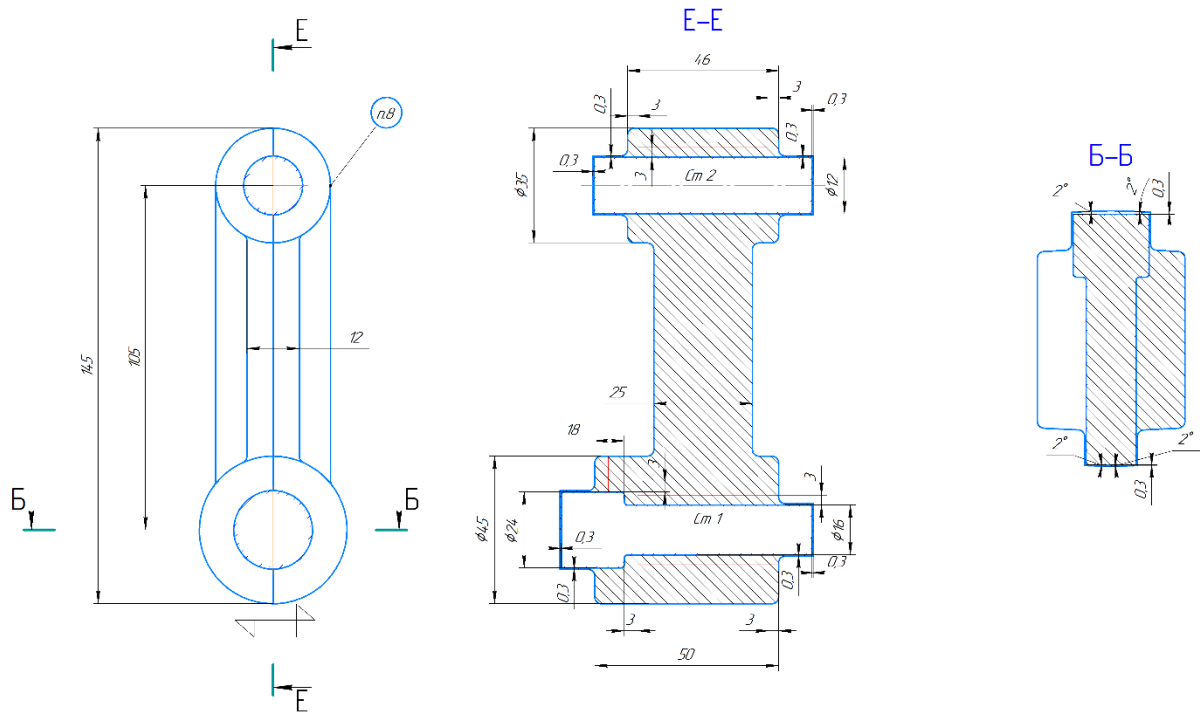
Робоче креслення відливка «Важіль»
